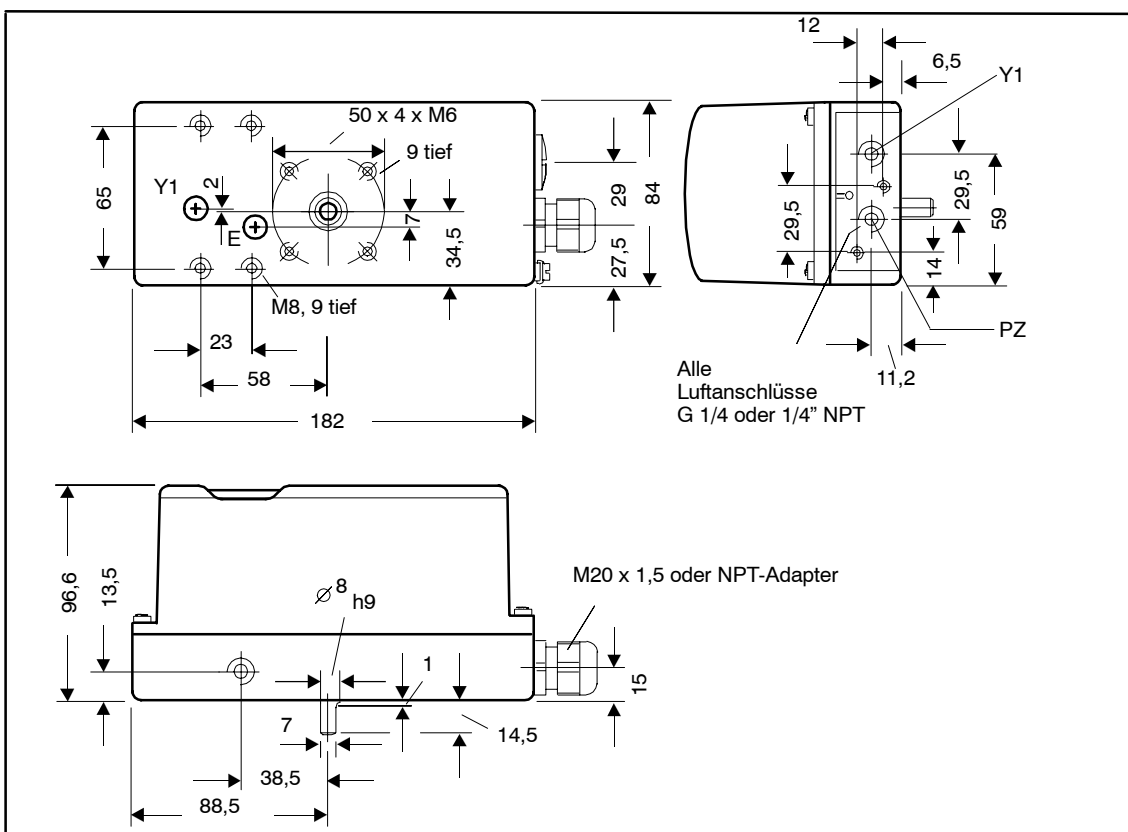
Maßbild Ausführung Metallgehäuse 6DR5xx1
